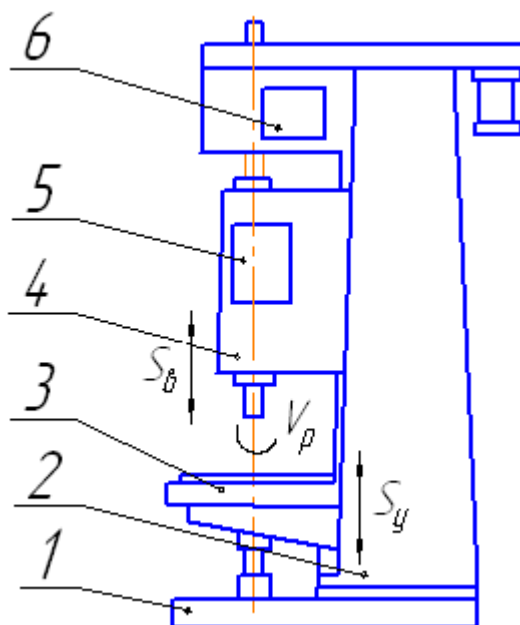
Вертикально-сверлильный станок модели 2Н150
